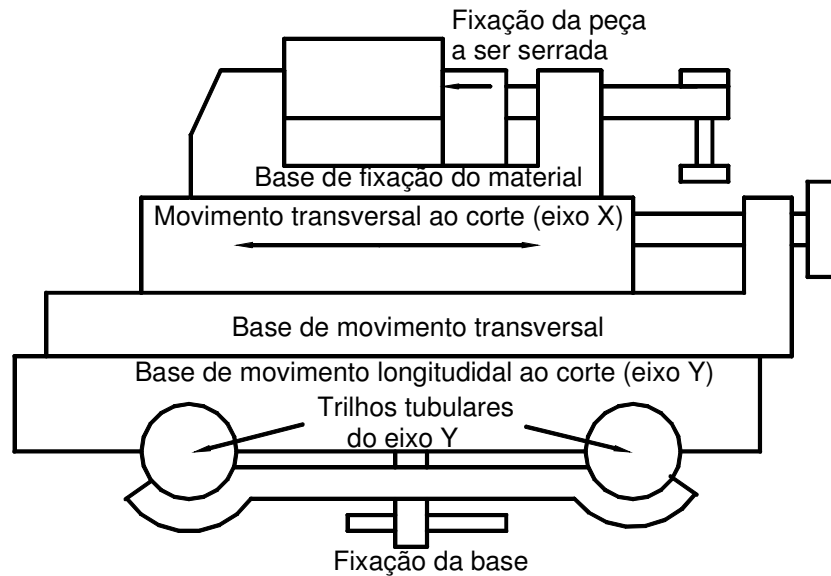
Desenho esquemático do conjunto que suporta a peça a ser cortada.
